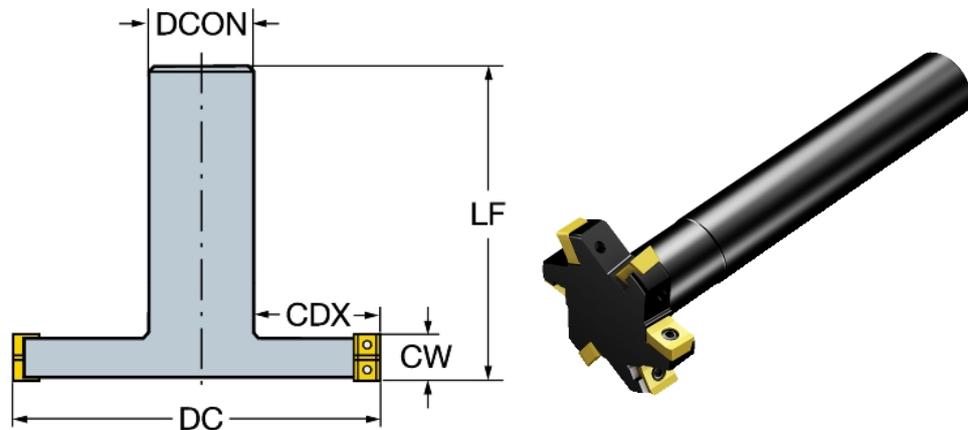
Фреза для фрезерования Т-образных пазов
